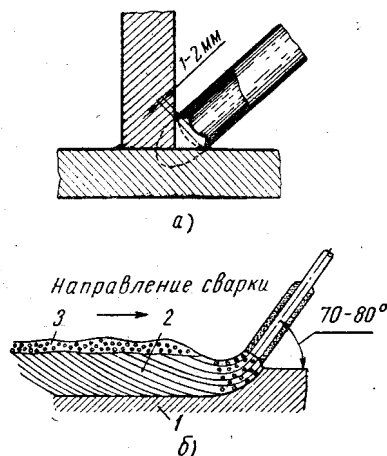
Положение электрода при сварке с глубоким проплавлением:
